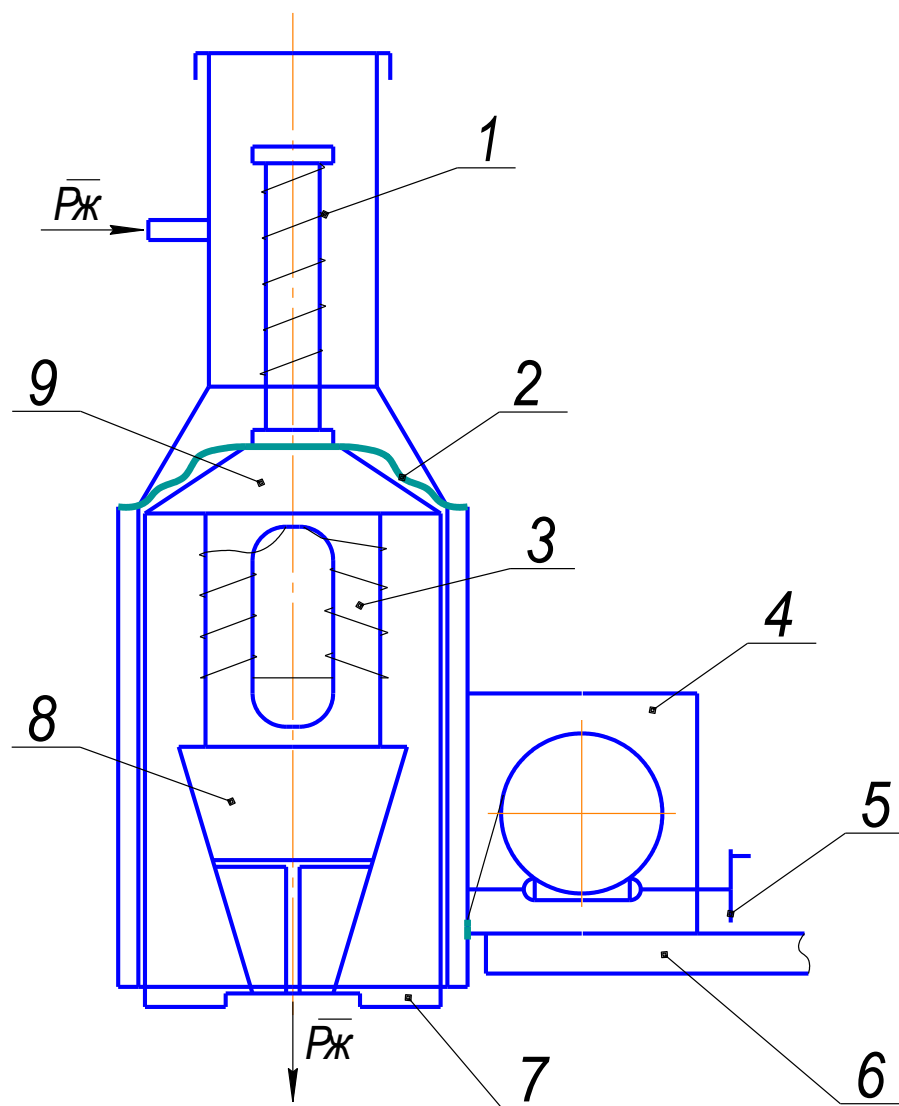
Схема устройства для ультразвуковой очистки шлифовального круга. 1 – пружина сжатия; 2 – резиноканевая диафрагма; 3 – магнестрикционный преобразователь; 4 – привод перемещения; 5 – рукоятка для ручного перемещения; 6 – установочная опора; 7 – гидростатический подпятник; 8 – волновод; 9 – подвижная часть устройства
